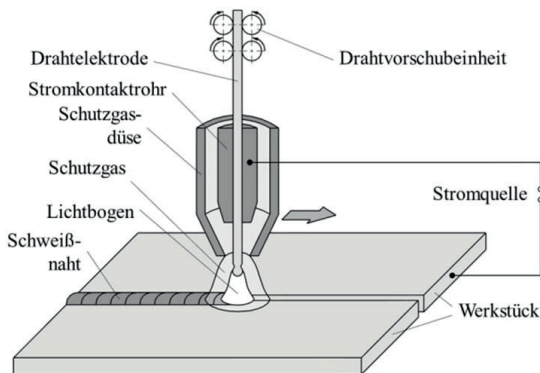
Verfahrensprinzip des MSG-Schweißens [MAT12]
